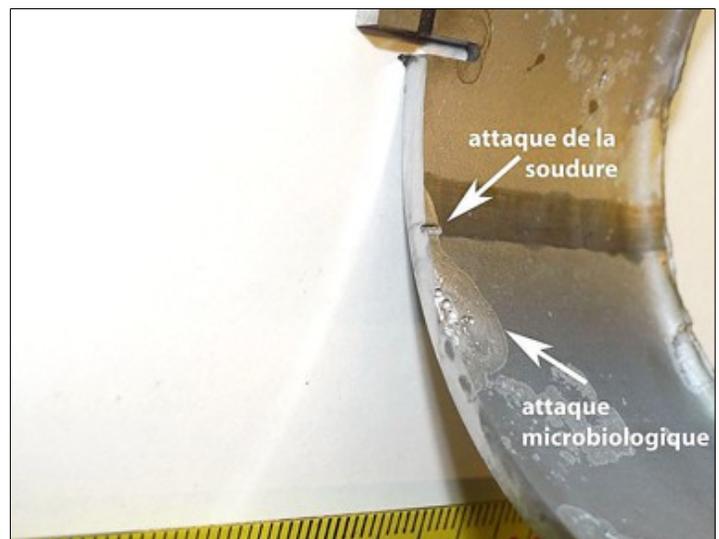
vue latérale de la coupe du tube après élimination de la rouille. Au-dessus, l'attaque préférentielle de la soudure est indiquée. L'autre attaque est microbiologique
